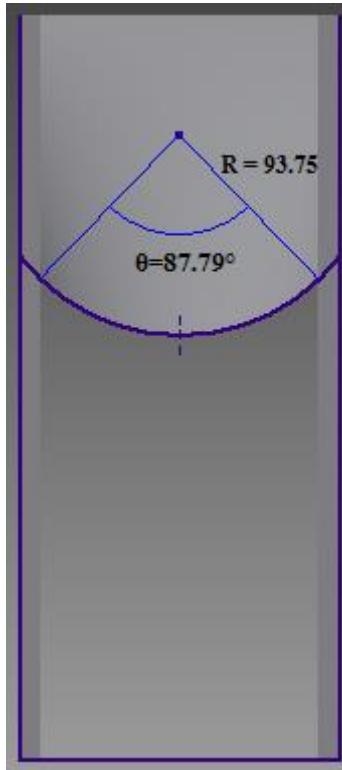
Vista frontal de la rampa. Fuente. Los autores
